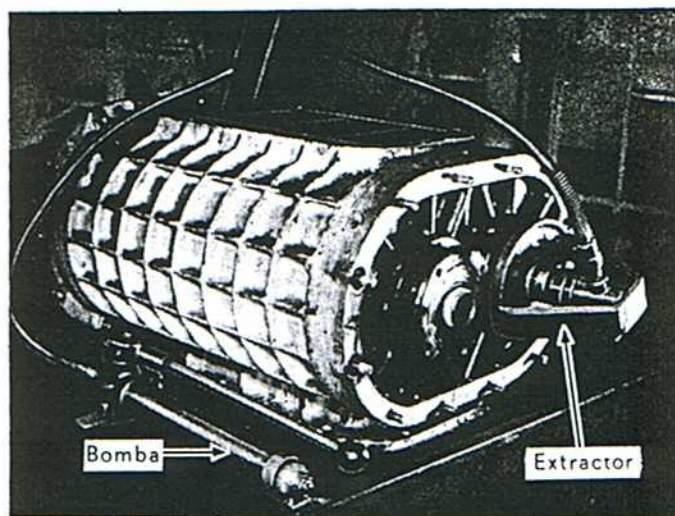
Forma de quitar los núcleos de los engranajes con un extractor hidráulico.
